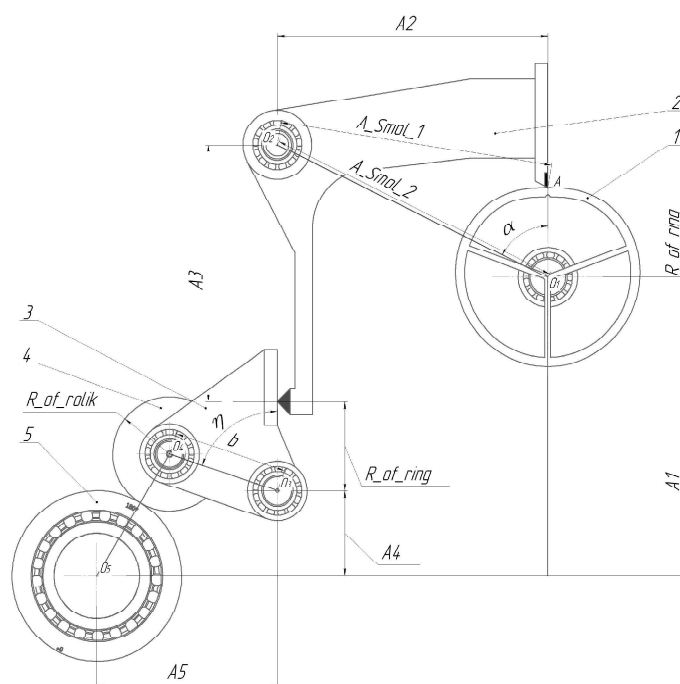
Кинематическая схема копировального узла токарно-фрезерного станка HCFX-2:
